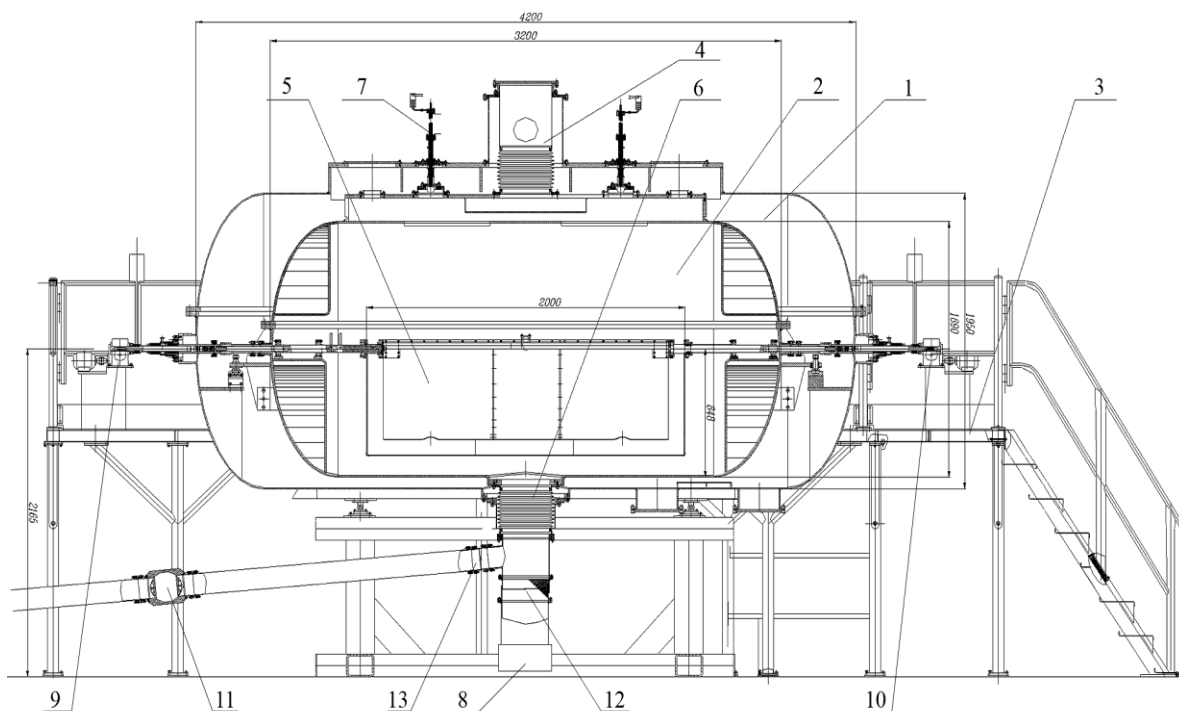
1 — Внешний вакуумный объём; 2 — внутренний вакуумный объём; 3 — платформа для обслуживания; 4 — откачка внутреннего сосуда; 5 — ловушка и вставка в нижнем положении; 6 — нейтроновод; 7 — система напыления ловушки и вставки; 8 — детектор; 9 — механизм поворота ловушки; 10 — механизм поворота вставки, 11 — затвор турбины, 12 — затвор детектора, 13 — затвор нейтроновода.
